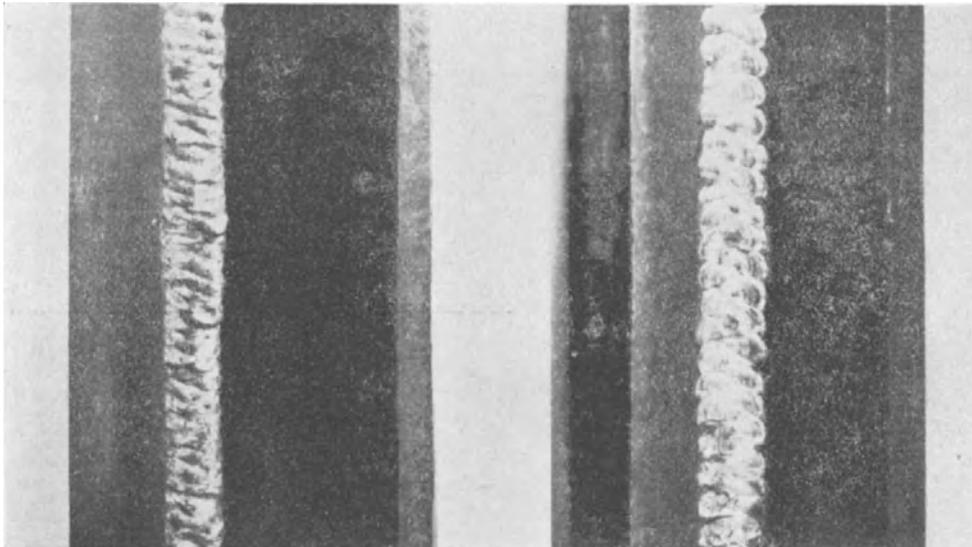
Senkrecht-Kehlnähte mit leicht ummantelten Elektroden von unten nach oben (links) und von oben nach unten (rechts) geschweißt.
